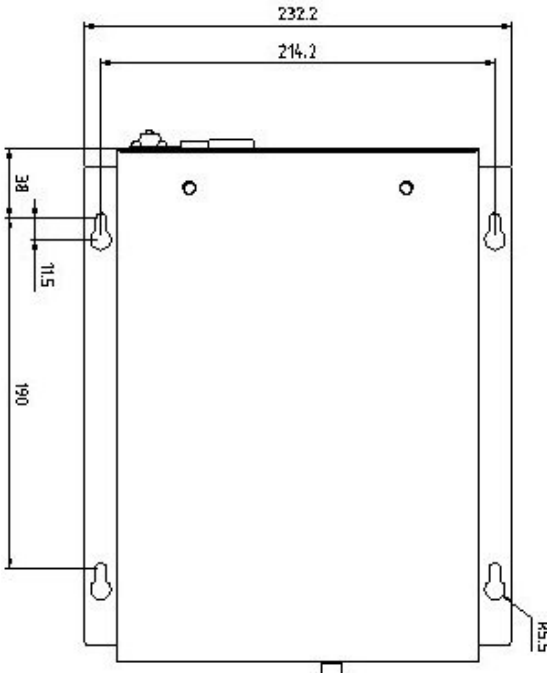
Lochbild für die Montage des Box PC SC-75_e
